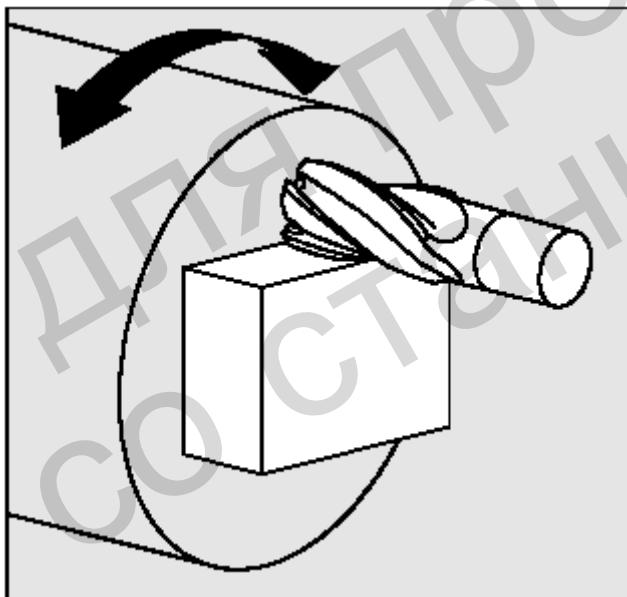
Фрезерная обработка на торцовой поверхности
